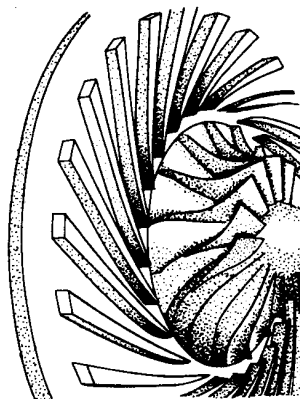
Рабочее колесо и каналный диффузор сверхзвуковой центробежной ступени [14]
